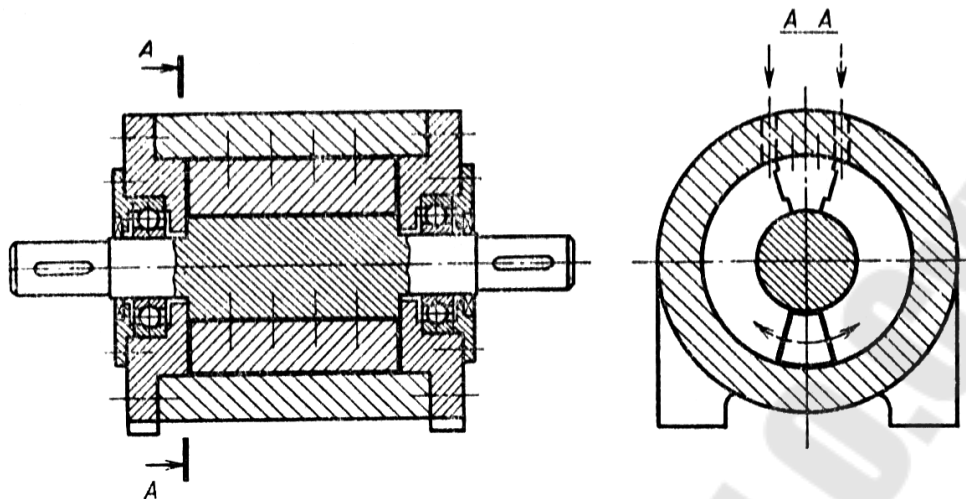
Пластинчатый гидроцилиндр с двусторонним валом
